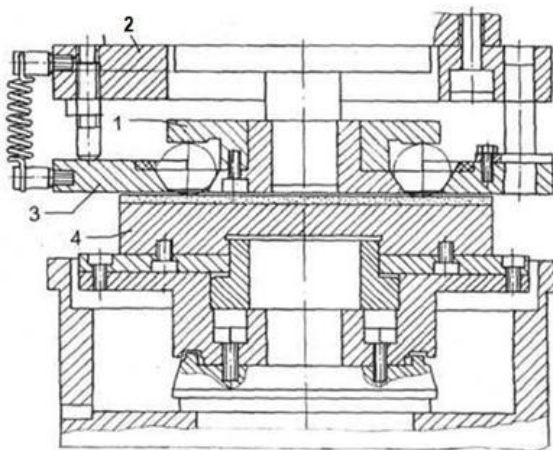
схема пристрою для шліфування куль з нижнім розташуванням інструмента: 1 – верхній диск; 2 – корпус; 3 – притискне кільце; 4 – шліфувальний круг.
